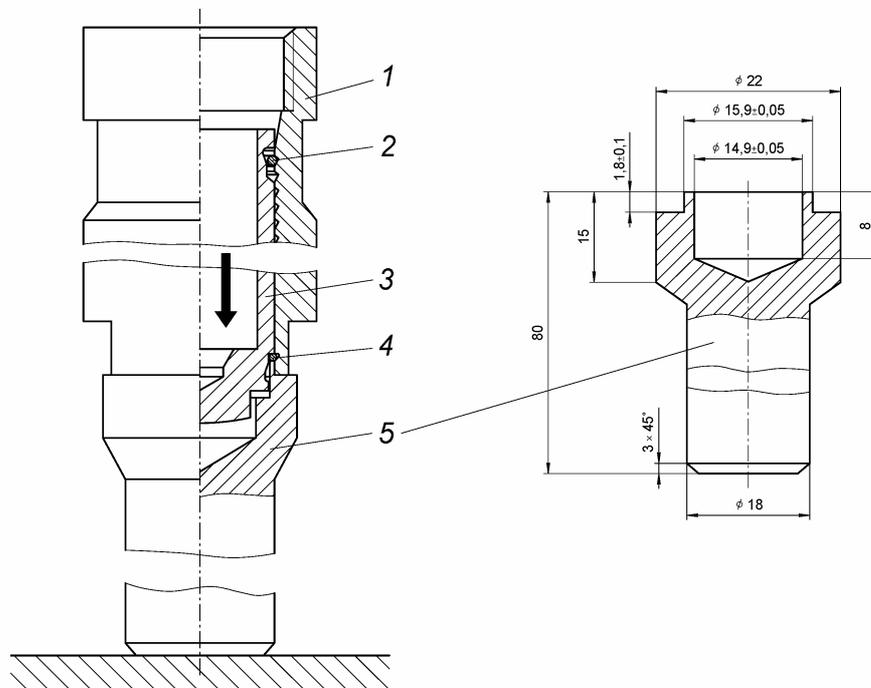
«Зарядка» гидронатяжителя с помощью оправки:
